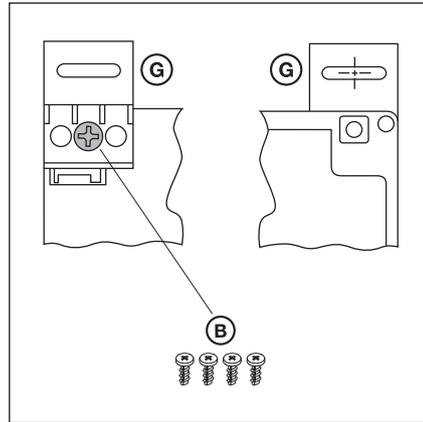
Befestigung der Montagefüße, Ansicht von hinten und vorne
